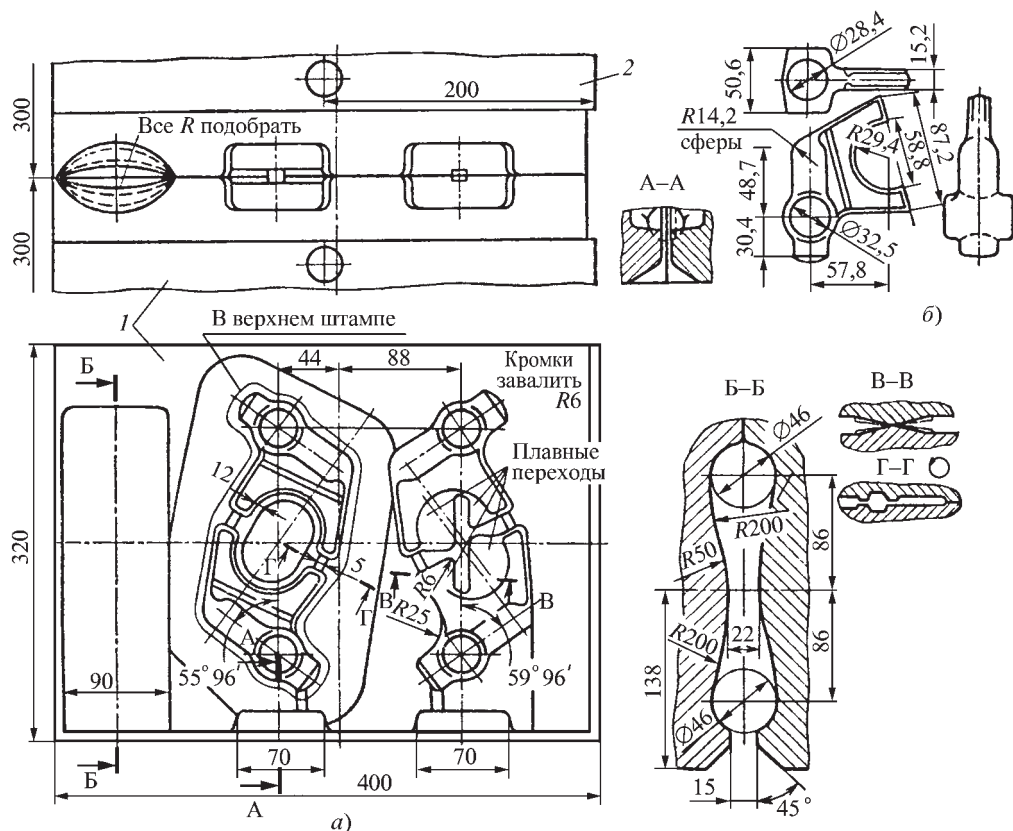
Молотовый штамп (а) и горячая поковка (б) вилки включения блокировки дифференциала: 1 — нижний штамп; 2 — верхний штамп
